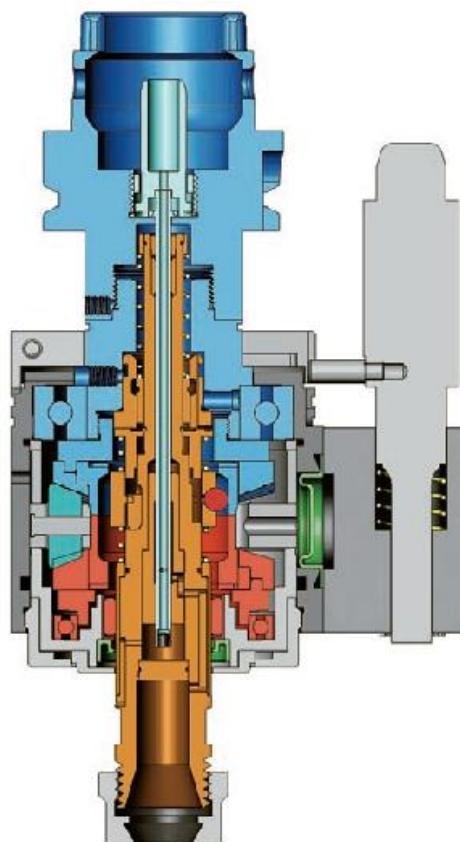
Реверсивный резьбонарезной патрон ТАРМАТИС
